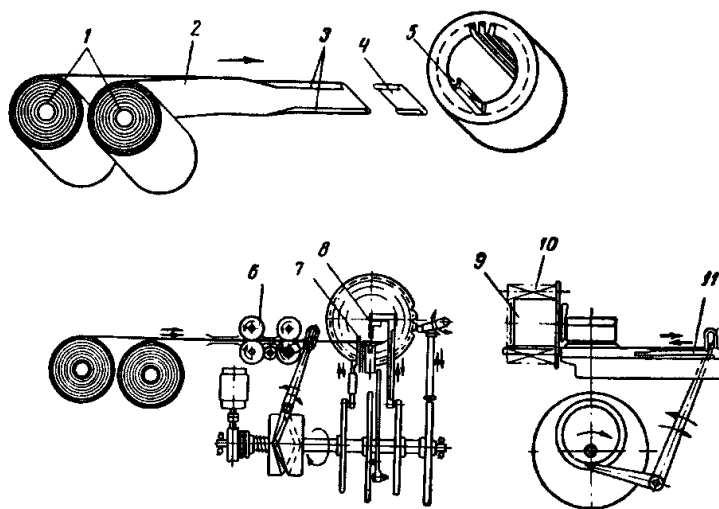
Кинематическая схема станка для изолировки пазов статора.
